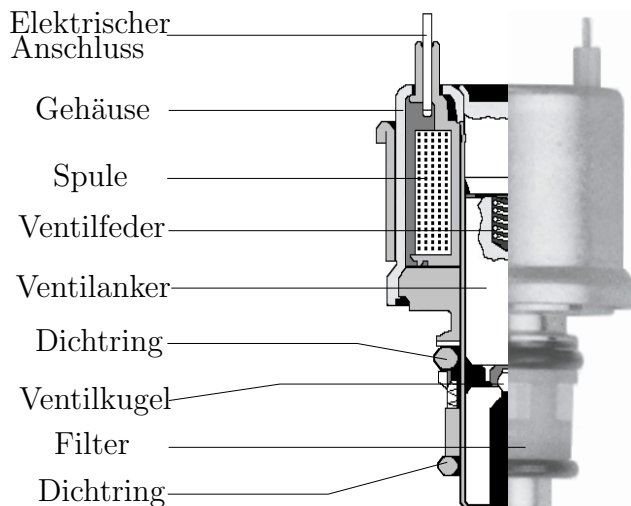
Aufbau des Auslassventils (Schaltventil) [Pos02].
